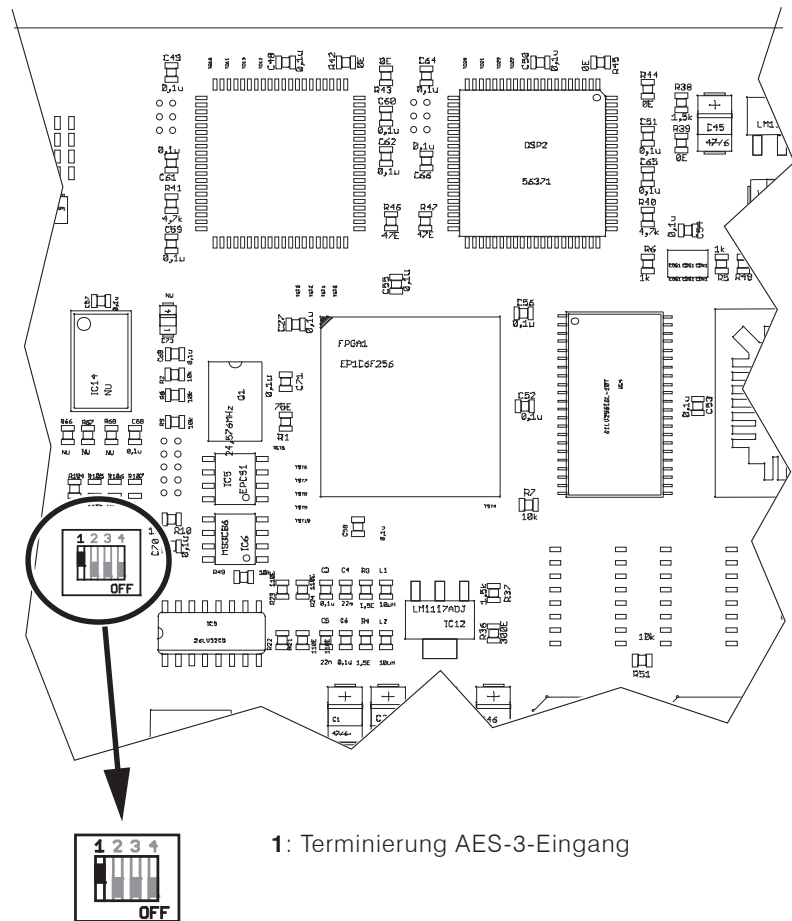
Teilansicht der Hauptplatine mit DIP-Schalter
